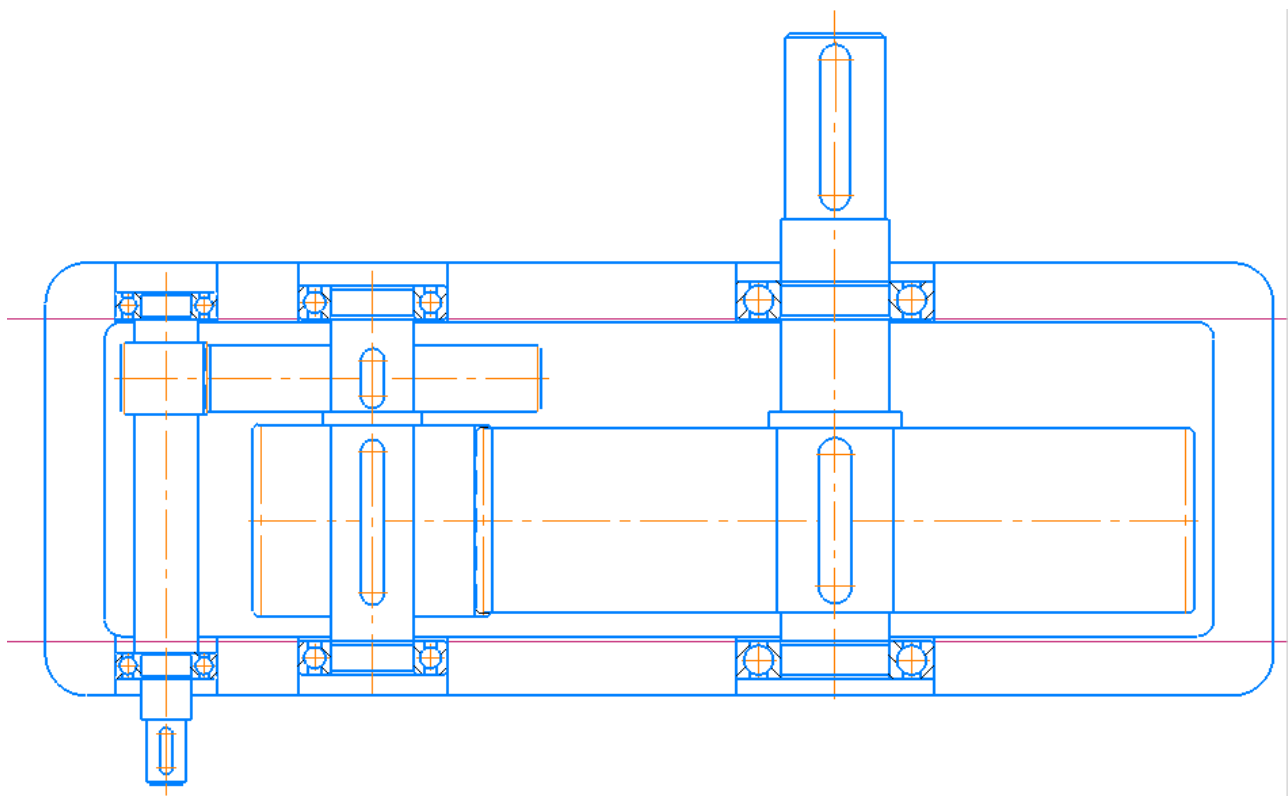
Ескіз площини рознімного з'єднання корпусу
